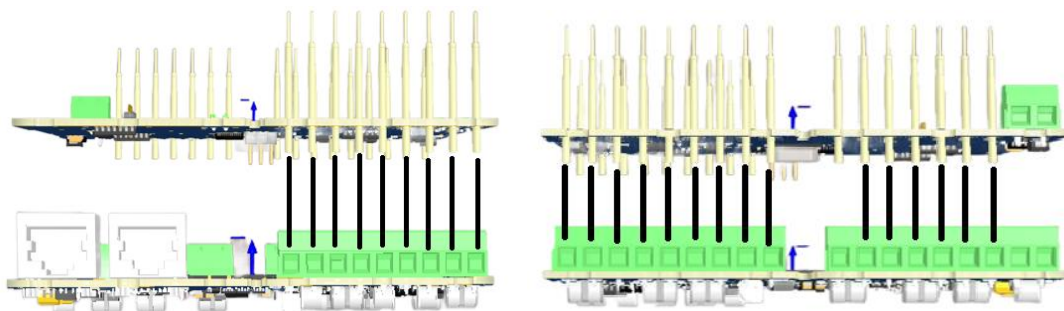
Referencia visual Conexionado PCB SmartGate y PCB externa
